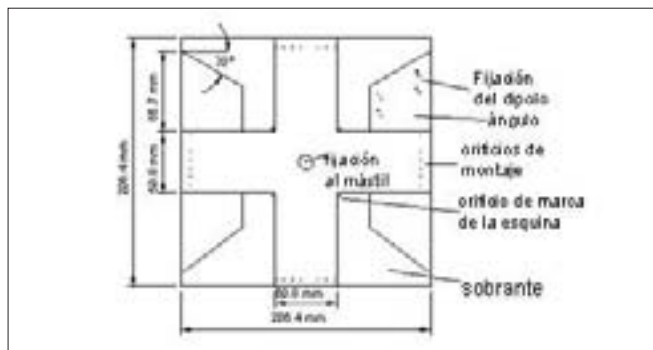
Plano de corte de una plancha de plexiglás u otro material apropiado de la que se pueden obtener todas las piezas necesarias para el montaje de la antena Lindenblad. Fuente: DL2LUX
